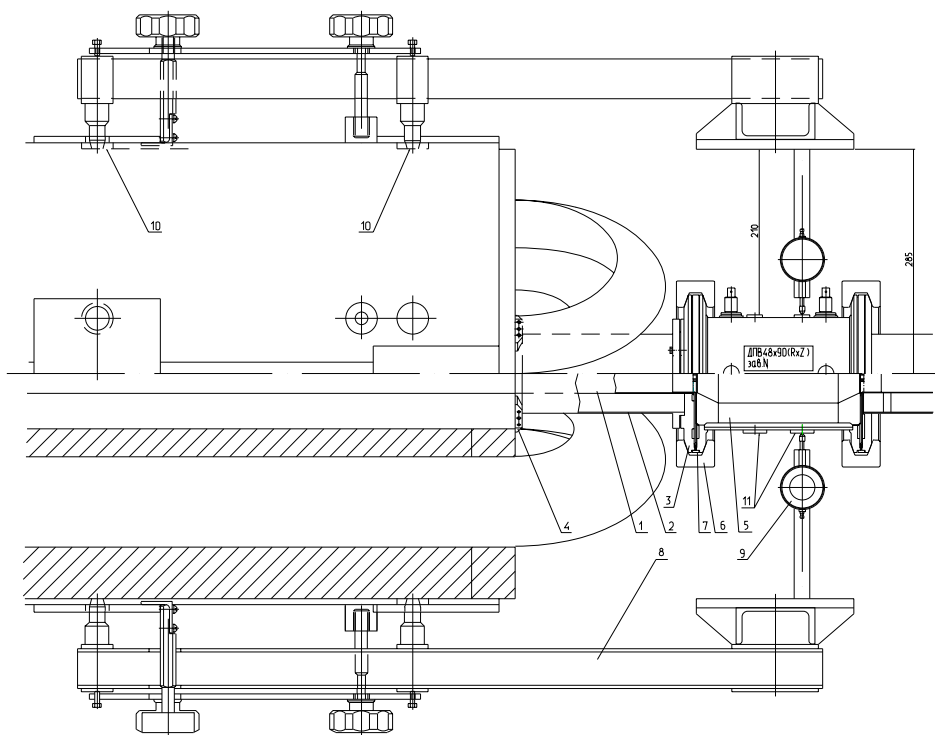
Схема установки датчика положения пучка на квадрупольной линзе. Условные обозначения: 1 — вакуумная камера линзы; 2 — стакан; 3 — фланец вакуумной камеры; 4 — сегмент; 5 — датчик положения пучка; 6 — стягивающий хомут быстроразъемного соединения; 7 — прокладка вакуумного уплотнения; 8 — штанга; 9 — измеритель; 10 — опоры штанги; 11 — геодезические реперы датчика положения.
